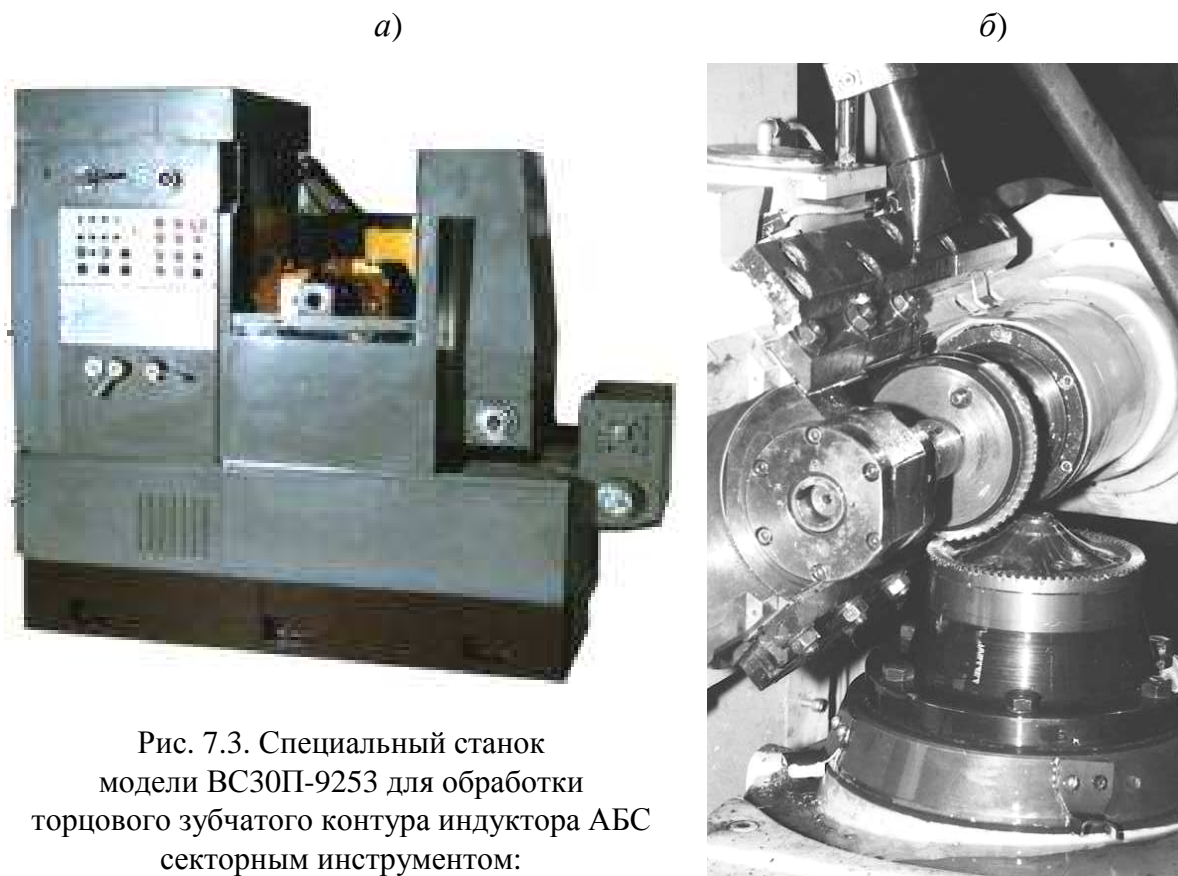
Специальный станок модели ВС30П-9253 для обработки торцового зубчатого контура индуктора АБС секторным инструментом:
